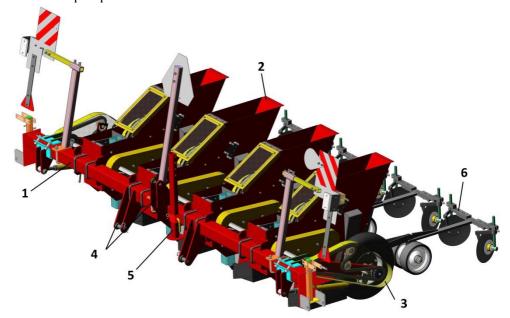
Общий вид машины для посадки лука-севка МПЛС
